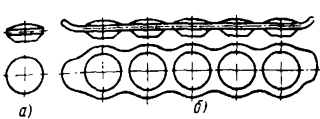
Способы штамповки поковки сателлита: а — по одной поковке; б — цепочкой
